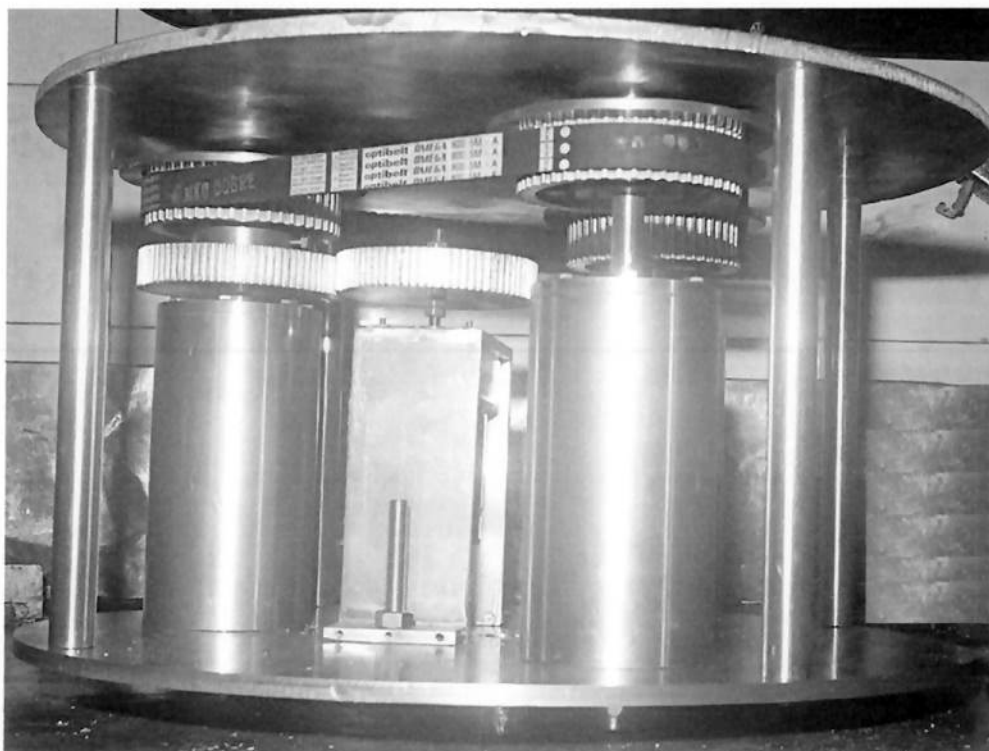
Peças fabricadas montadas entre as placas superior e inferior.
